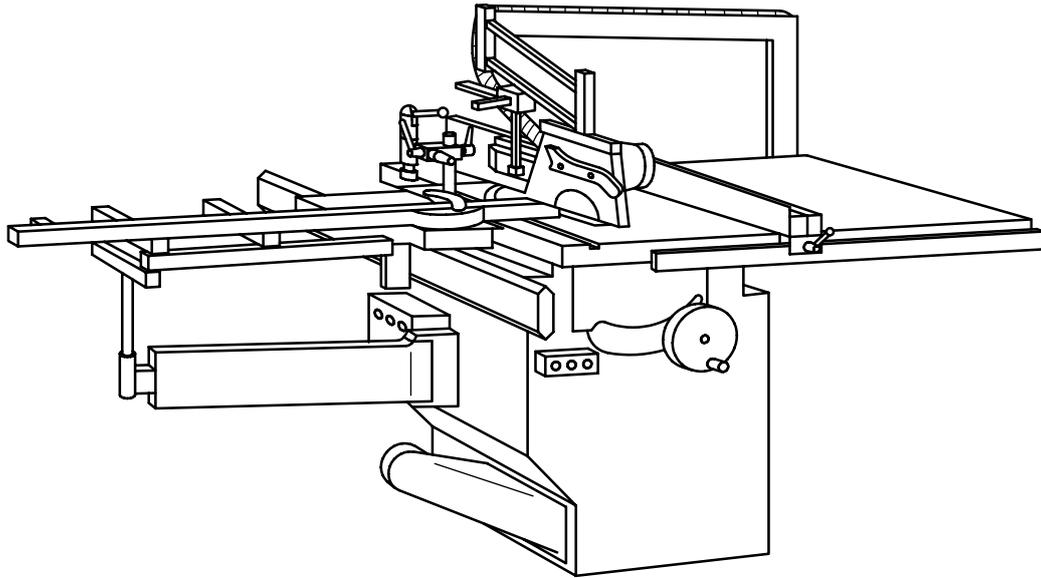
Exemple d'une machine avec unité de sciage à table et unité de toupillage, équipée d'une table mobile
